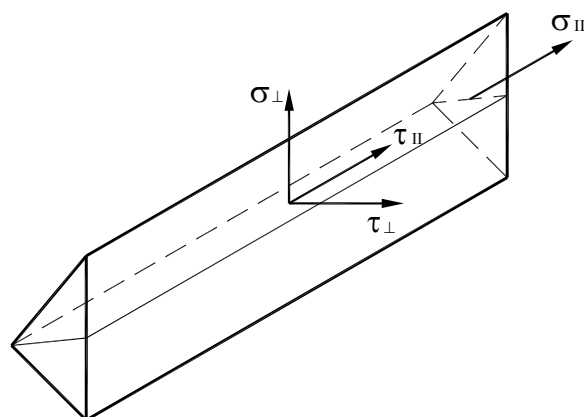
Напряжения в поперечном сечении углового сварного шва
